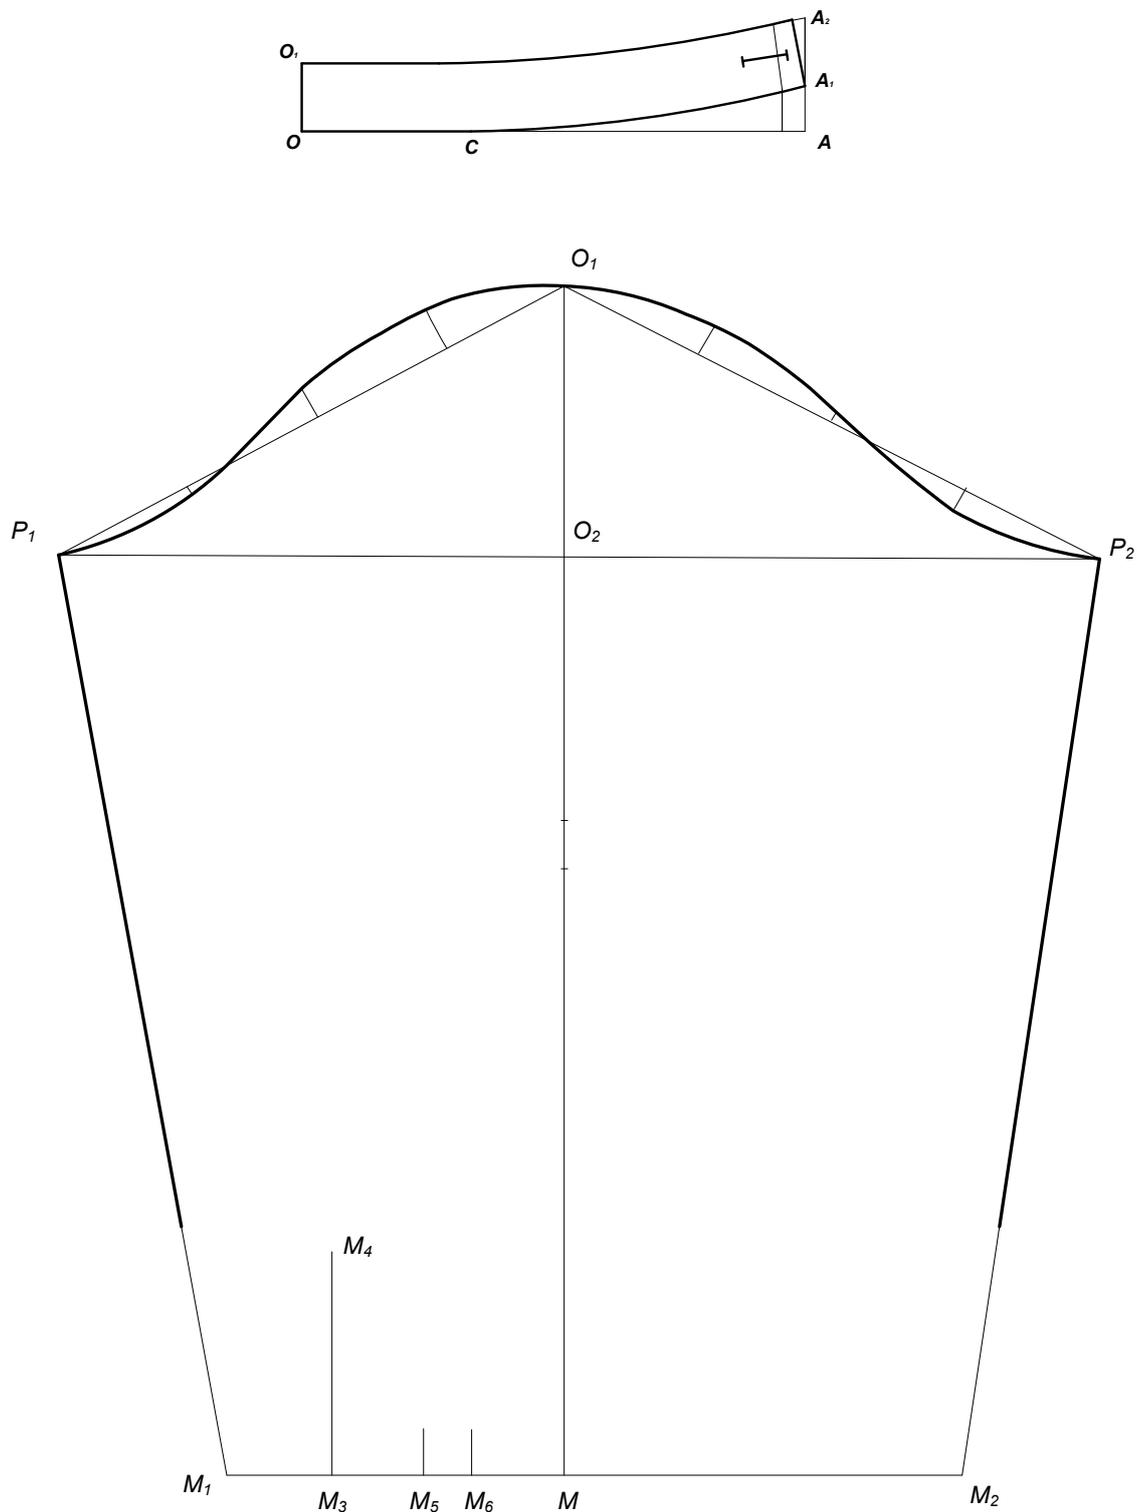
Чертеж БК рукава и воротника стойка
